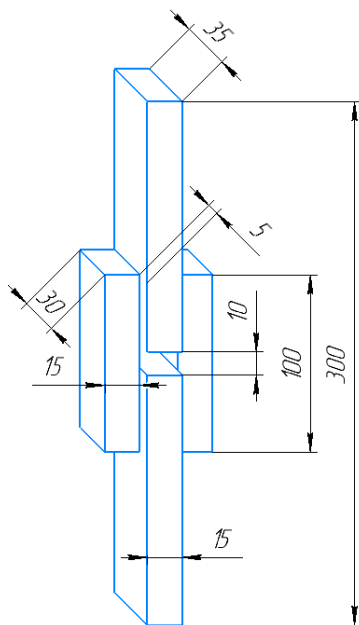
Загальний вигляд зварного зразка з накладками
